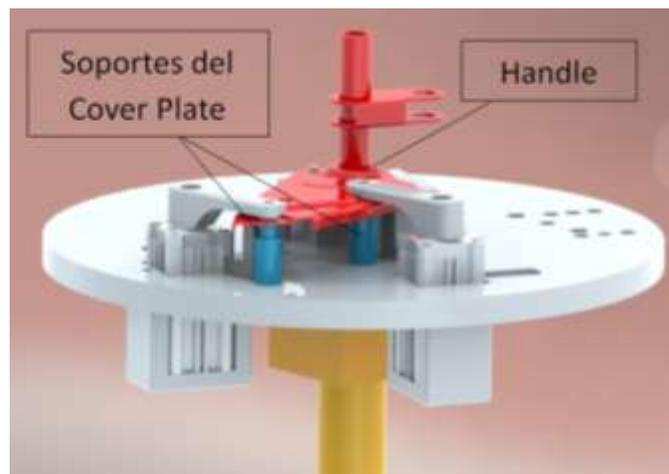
Primer diseño de soportes del “Cover – plate” del handle.
